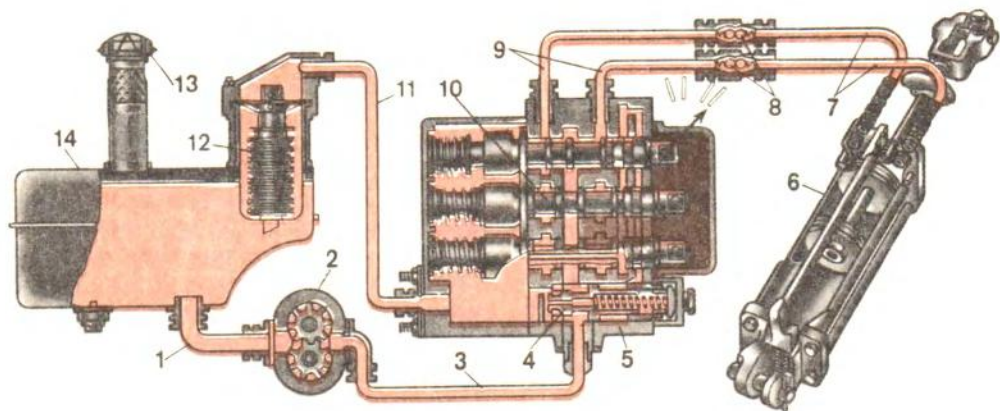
Схема раздельно-агрегатного гидропривода механизма навески трактора:
